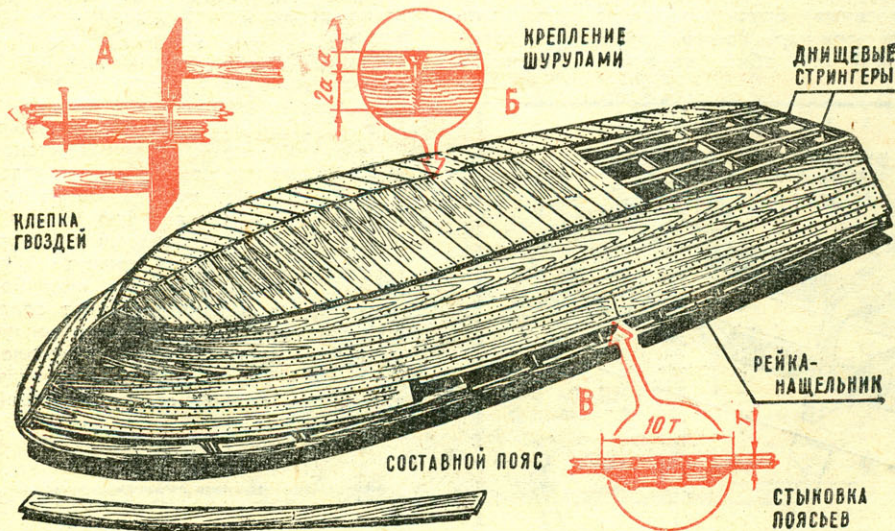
Обшивка наката досками (дно — тарная доска поперек, борта — долевые пояса): А — клепка гвоздей «взагиб», Б — крепление досок шурупами «впотай», В — соединение долевых поясов обшивки.
